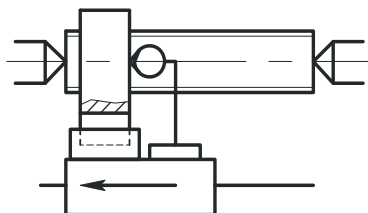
Схема проверки кинематической точности винторезной цепи
